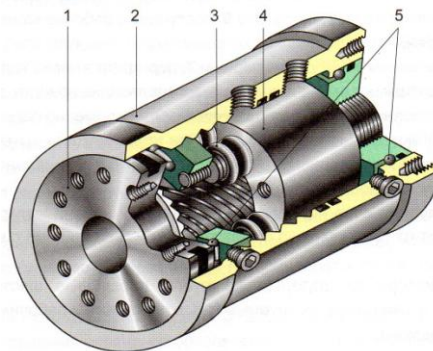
, г. Поршневой ПГД с винтовым преобразователем: 1 – вал; 2 – корпус; 3 – ролики; 4 – поршень; 5 – радиально-упорные подшипники.
